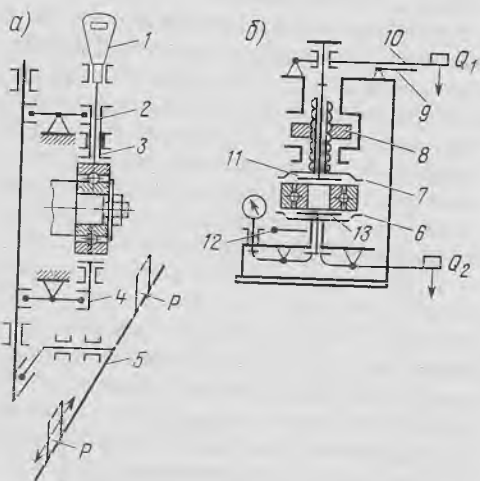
Приспособление для контроля зазоров шариковых подшипников
